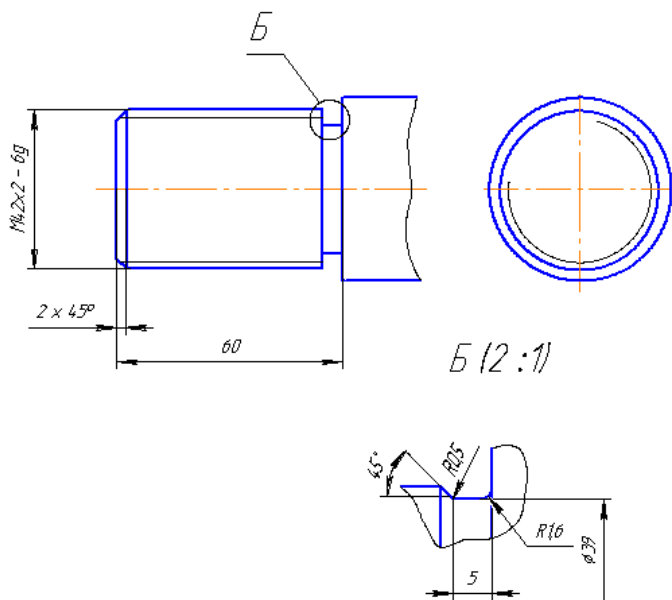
Изображение наружной резьбовой проточки на чертеже
